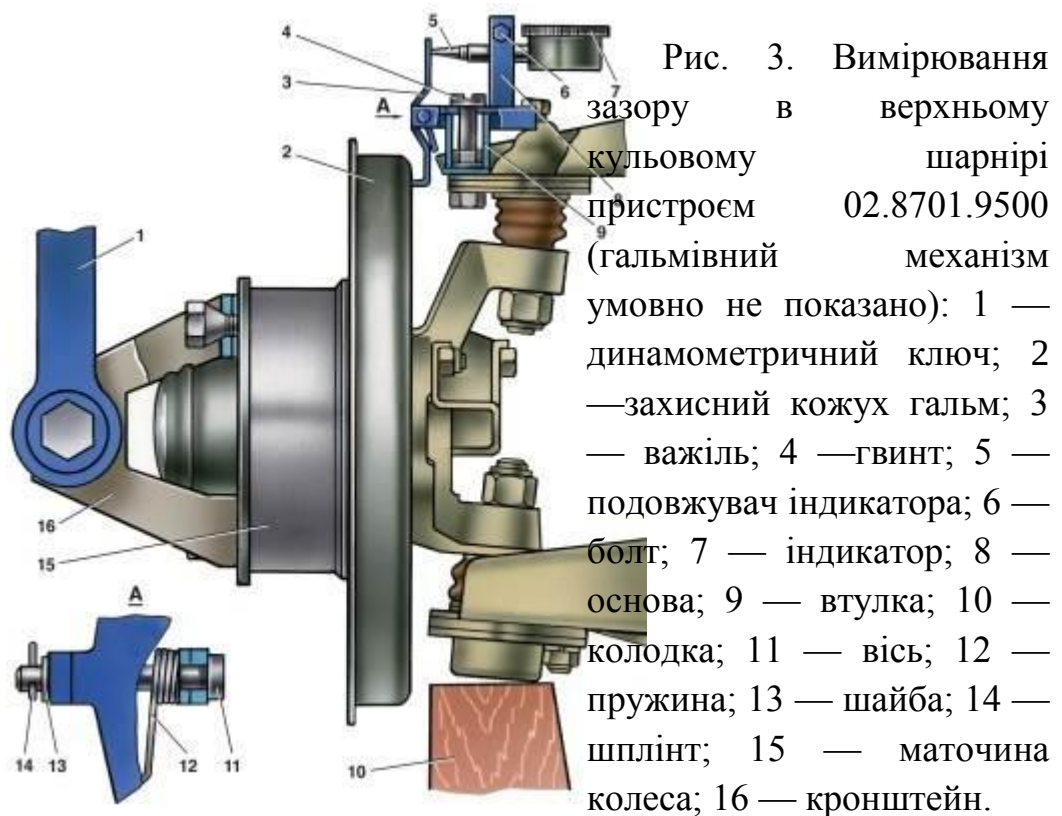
Вимірювання зазору в верхньому кульовому шарнірі пристроєм 02.8701.9500 (гальмівний механізм умовно не показано): 1 — динамометричний ключ; 2 — захисний кожух гальм; 3 — важіль; 4 — гвинт; 5 — подовжувач індикатора; 6 — болт; 7 — індикатор; 8 — основа; 9 — втулка; 10 — колодка; 11 — вісь; 12 — пружина; 13 — шайба; 14 — шплінт; 15 — маточина колеса; 16 — кронштейн.
